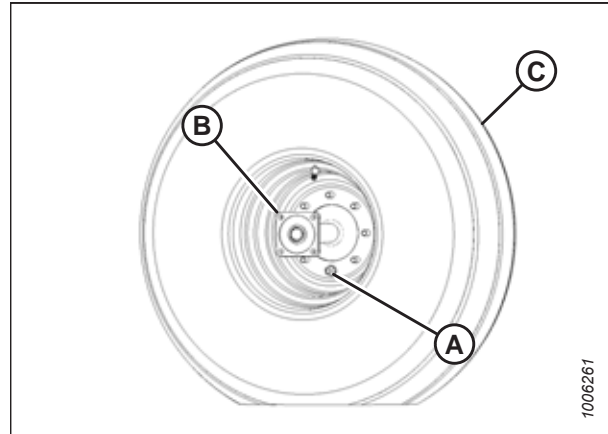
Вилочное самоустанавливающееся колесо
